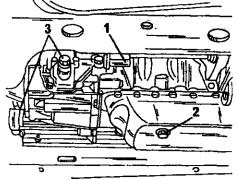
Вид снизу двигателя и коробки передач с расположением сливных пробок.
